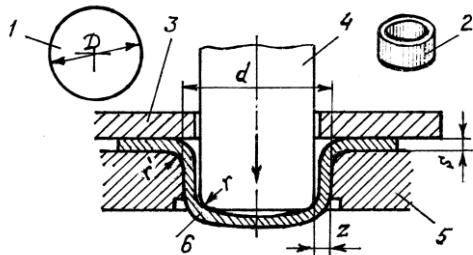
Схема вытяжки: 1 – исходная заготовка; 2 – изделие; 3 – прижим; 4 – пуансон; 5 – матрица; 6 – формируемая заготовка ( $D$  – диаметр исходной заготовки;  $d$  – диаметр изделия;  $s$  – толщина заготовки;  $z$  – зазор между пуансоном и матрицей)
